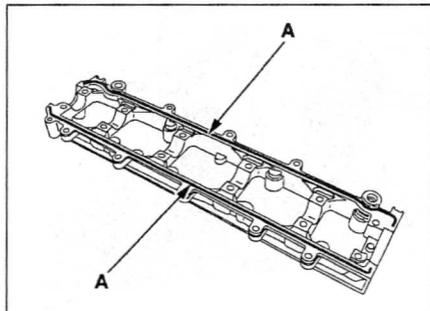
Нанесите герметик в виде узкого валика (А) на сопрягаемую поверхность корпуса подшипников распределительного вала, как показано (двигатели 2.0 л)
